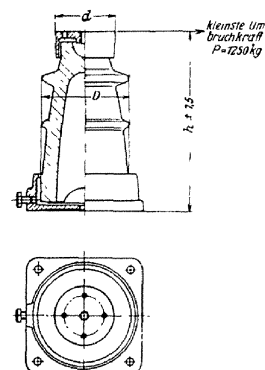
VDE-Stützer der Gruppe C für Innenräume für 1250 kg Umbruchkraft mit quadratischem Sockel.
